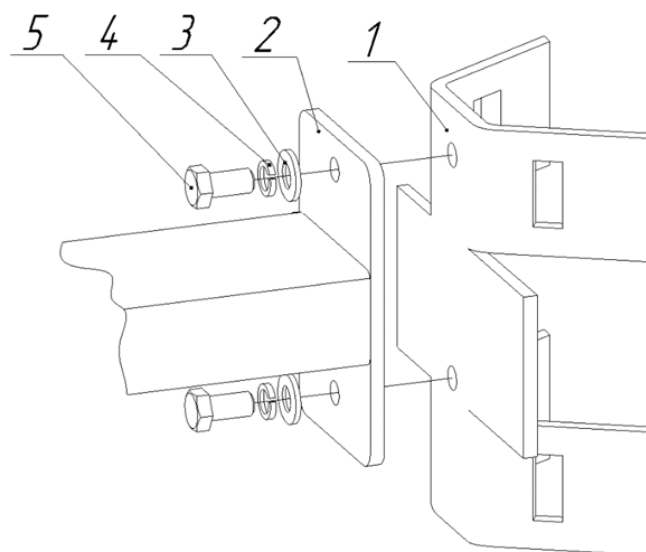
Конструкция устройства крепления приемопередатчика
